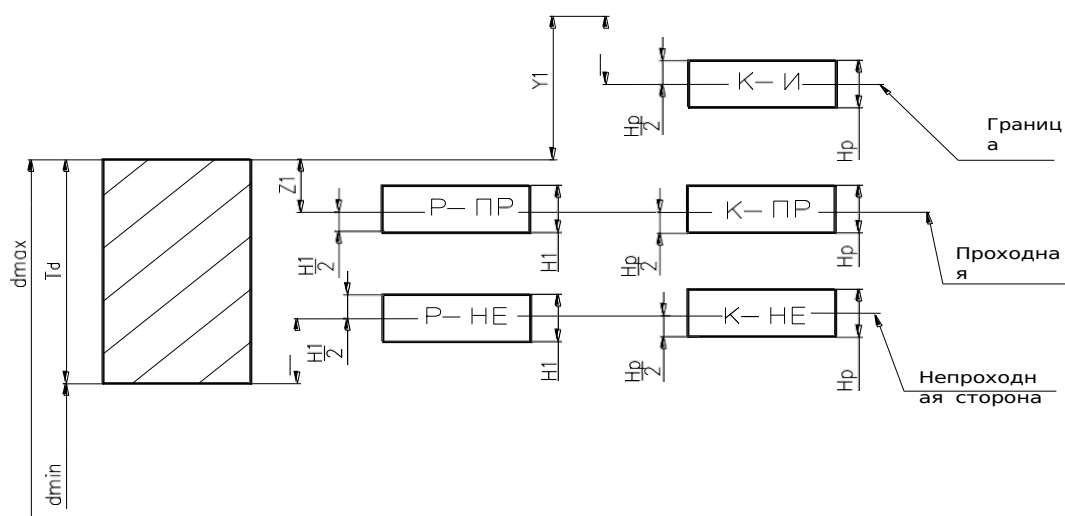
Схемы полей допусков для вала и калибров-скоб
